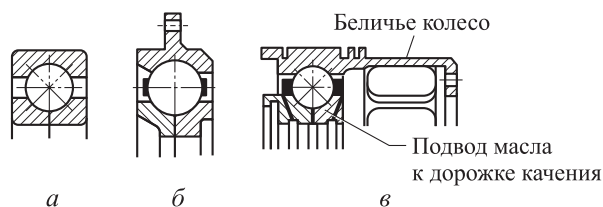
Развитие конструкции подшипников главного вала авиационного двигателя [1]
